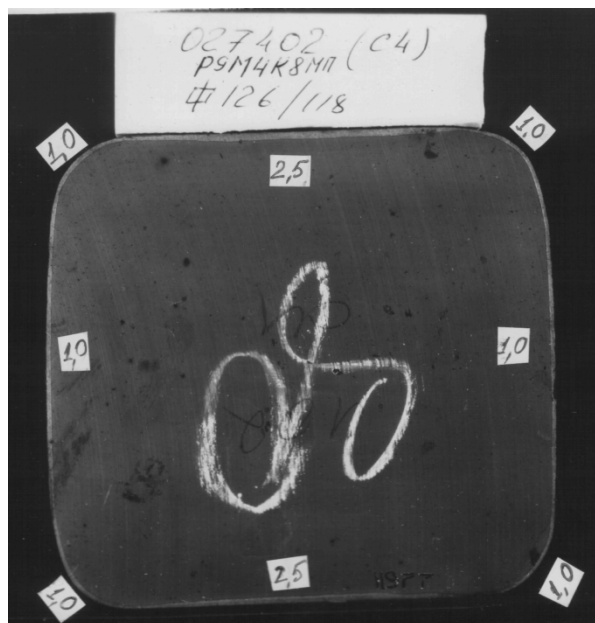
Распределение обечайки на поверхности катаной заготовки кв. 126 мм стали P9M4K8-MП
